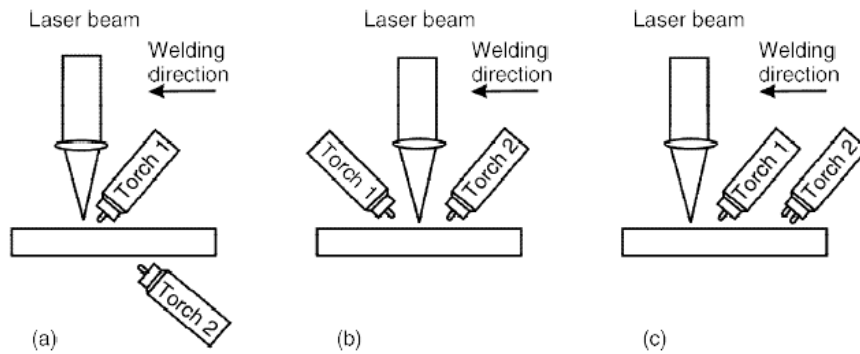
Representação esquemática do processo de soldadura híbrido com duas fontes de calor secundárias, [8].
